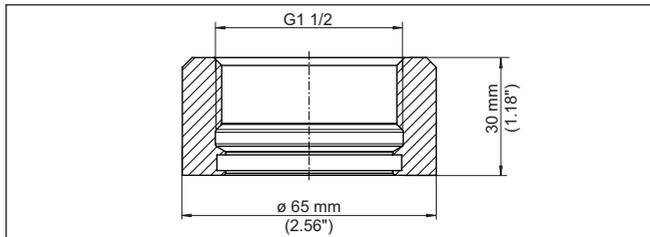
Dimensiones racor para soldar rosca G1½ (ISO 228-1) - Diseño higiénico
